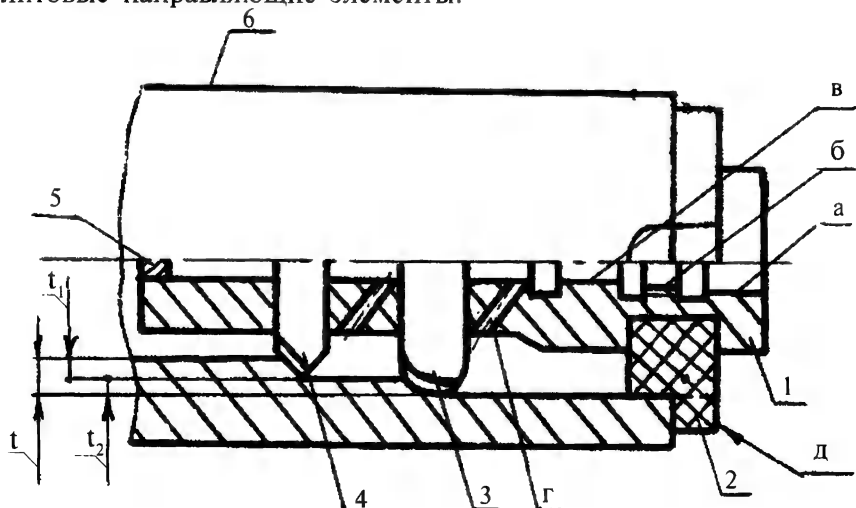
Двухрезцовая расточная головка с односторонним расположением резцов: 1 - корпус головки, 2 - шпонка, 3 - чистовой резец, 4 - получистовой резец, 5 - черновой резец, 6 - пробка, 7 - обрабатываемая деталь
